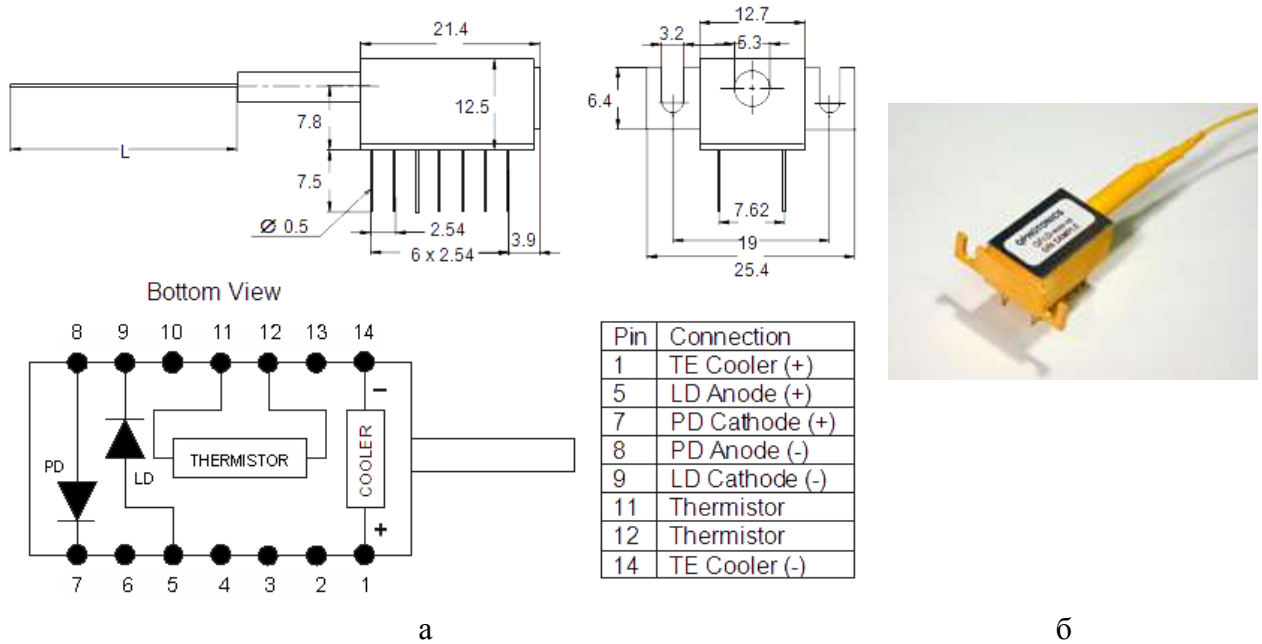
Габаритный чертеж и принципиальная схема передающего модуля (а) и его внешний вид (б)
